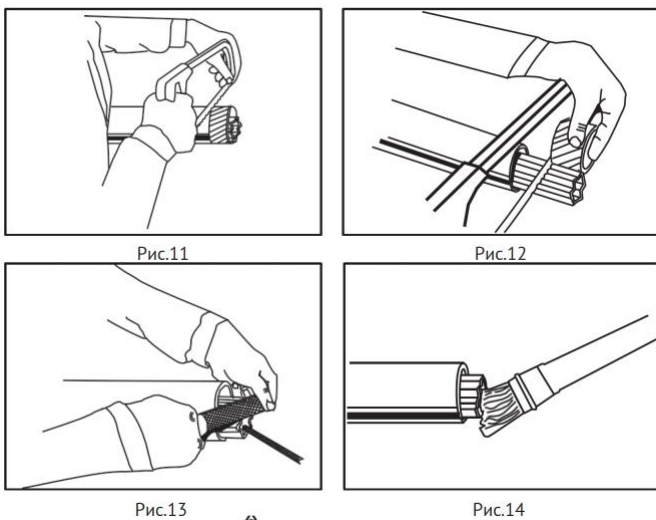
14 Последовательность подгонки карданного вала по длине: разметка, укорочение, зачистка кромок, смазка и сборка
